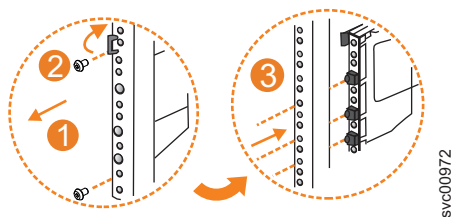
Remova a montagem de trilho do suporte da estrutura frontal
